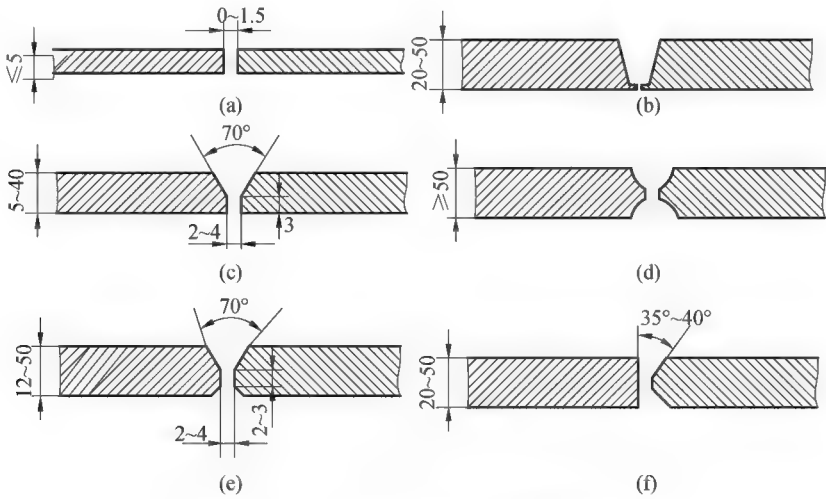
坡口形式及其适用的焊接件厚度
